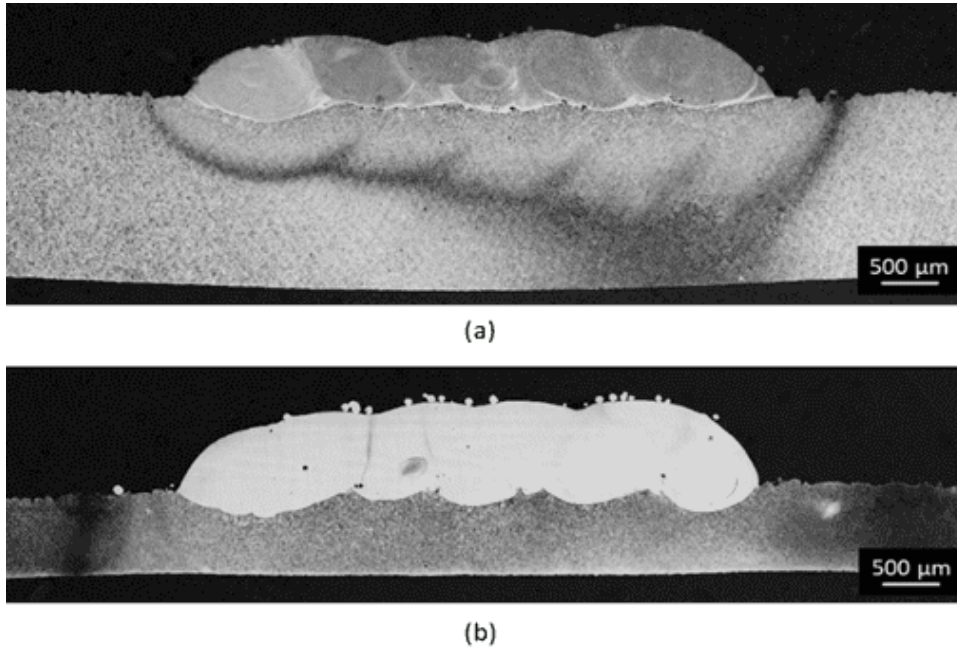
Secções transversais das camadas fabricadas: (a) n.6 e (b) n.7.
